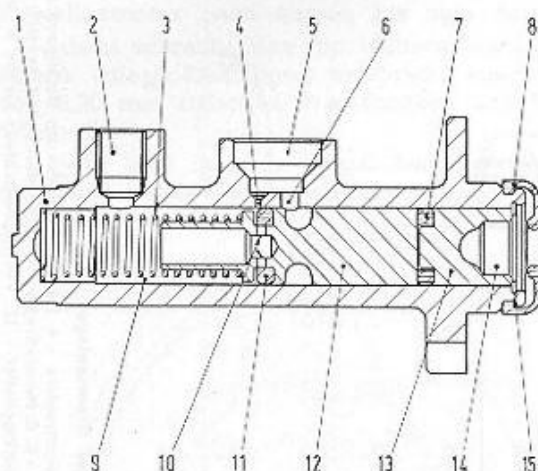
Längsschnitt durch den Hauptbremszylinder.
